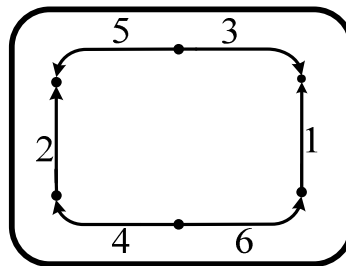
Последовательность наложения сварных швов одним сварщиком
